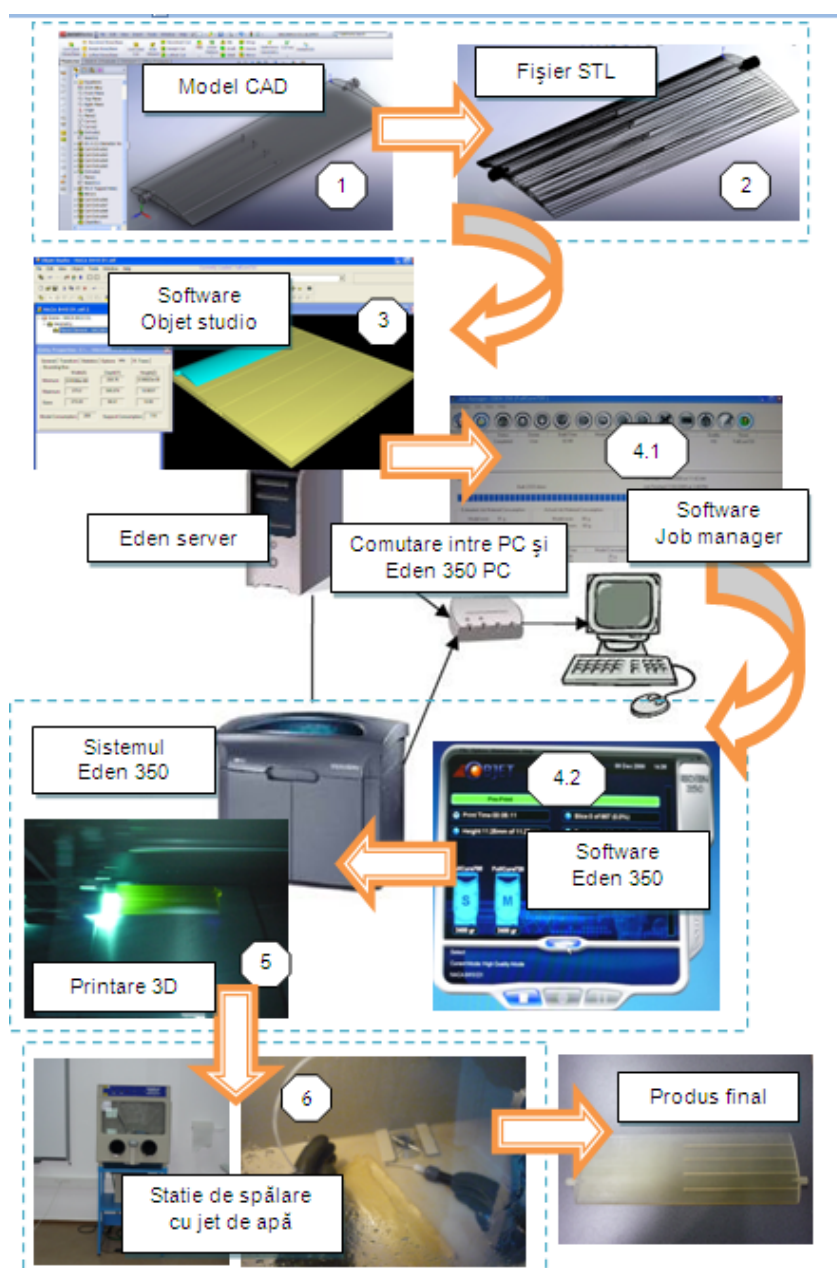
Procesul de fabricație aditivă pe EDEN 350 [21, 22]
